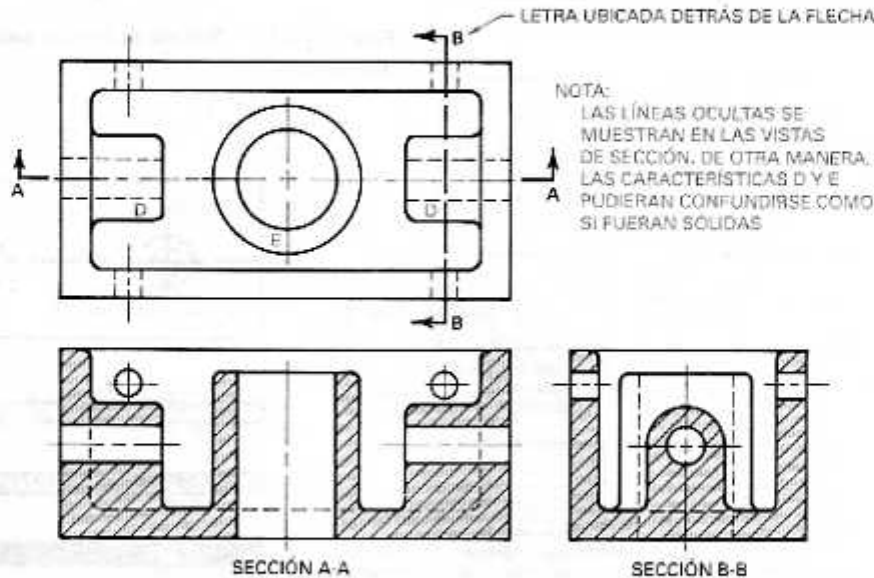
Dibujo detallado con dos vistas en corte.
